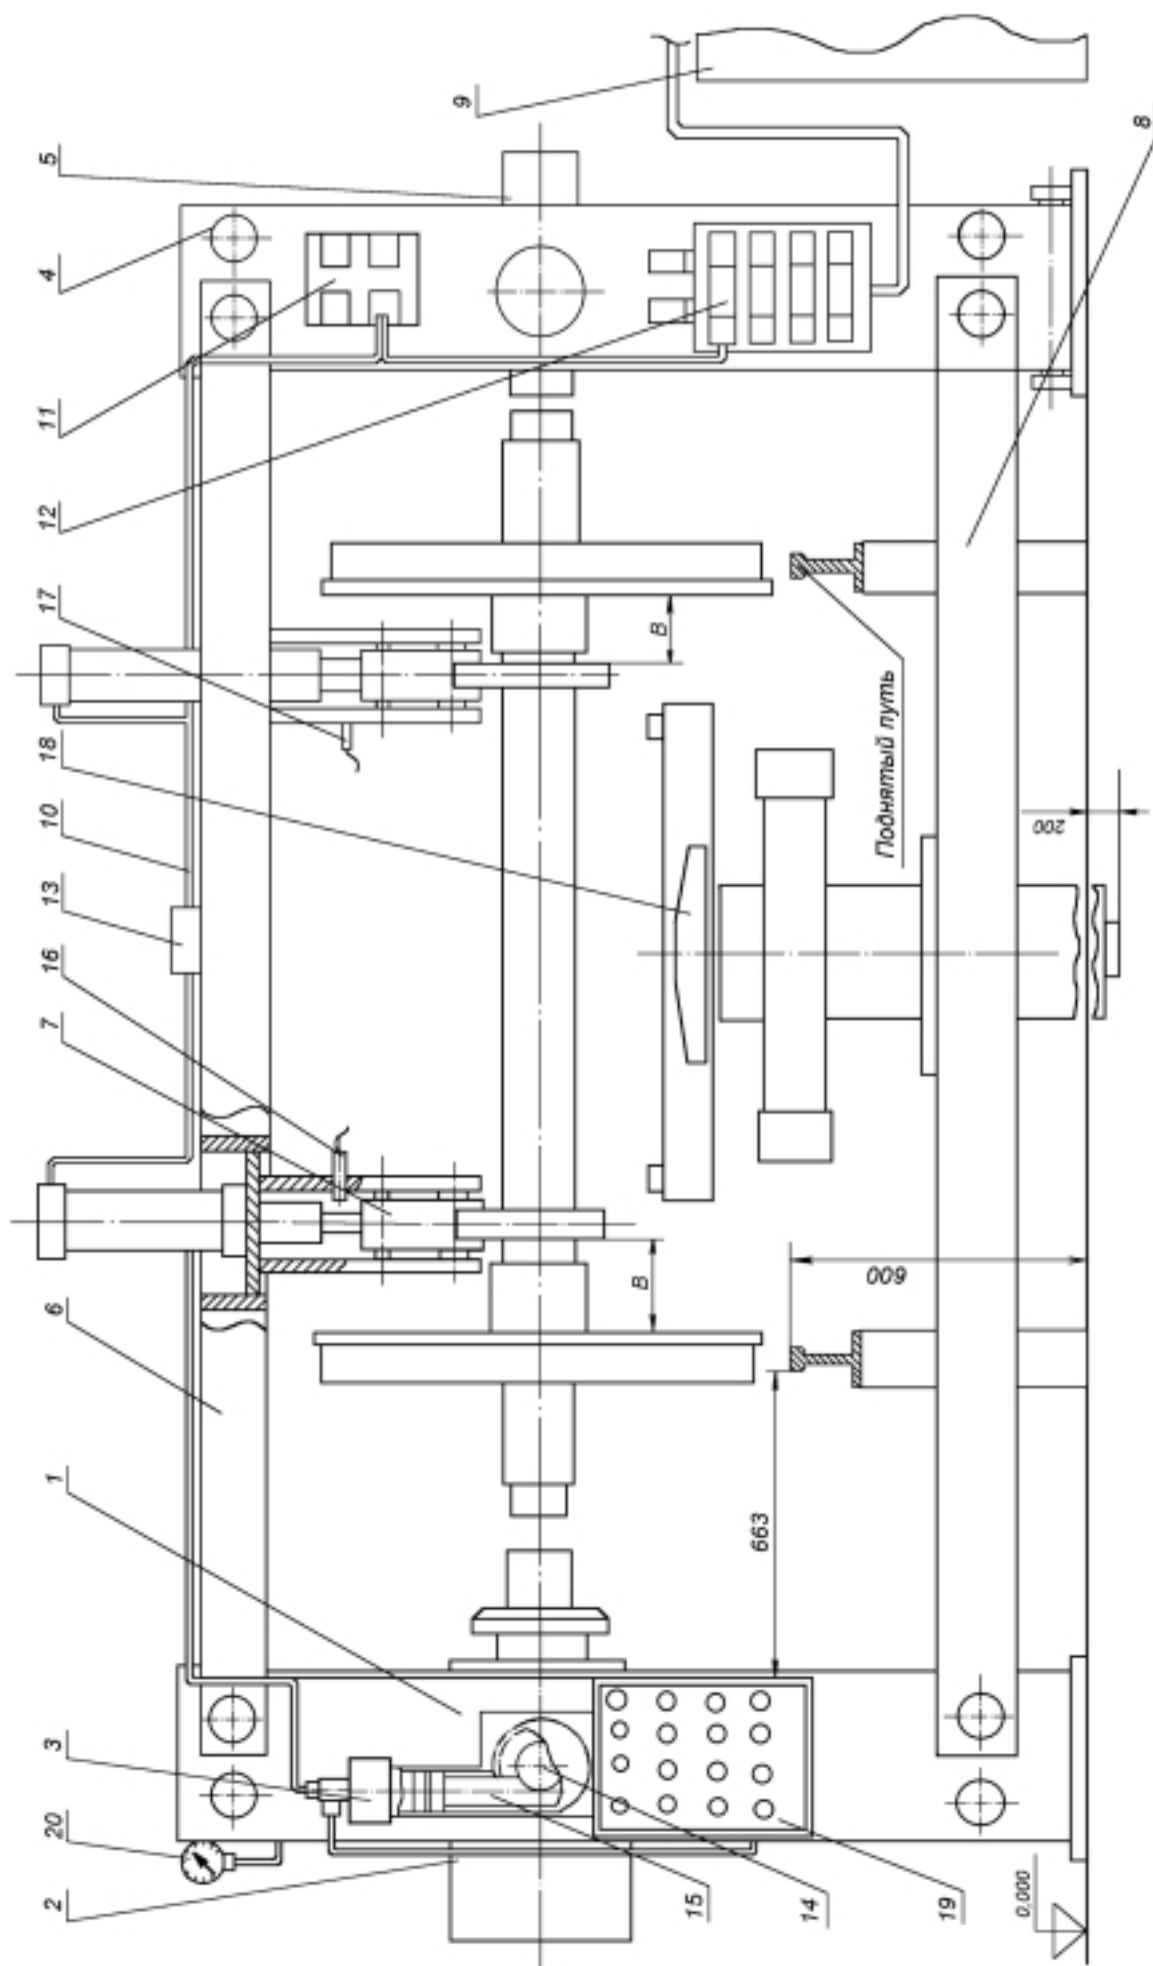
Установка для холодной напрессовки подшипников ГД-206
